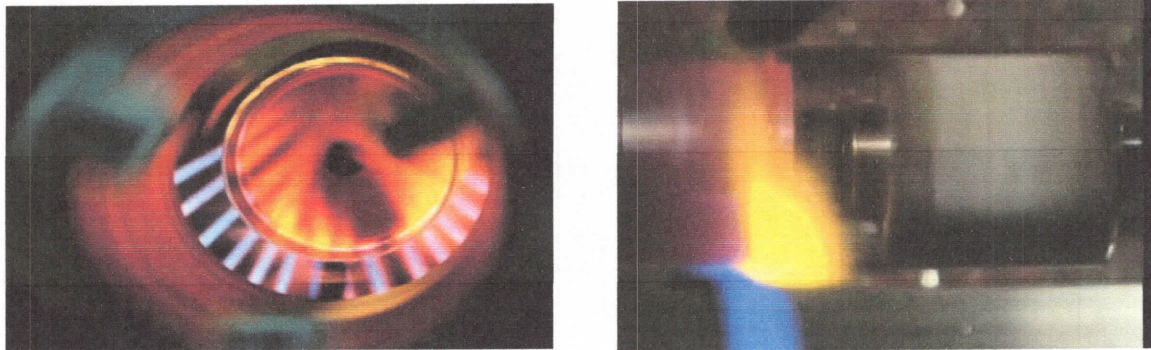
Le soudage de fonte usiné tout en fabriquant un joint de tube solaire en employant la technique flamboyante.
